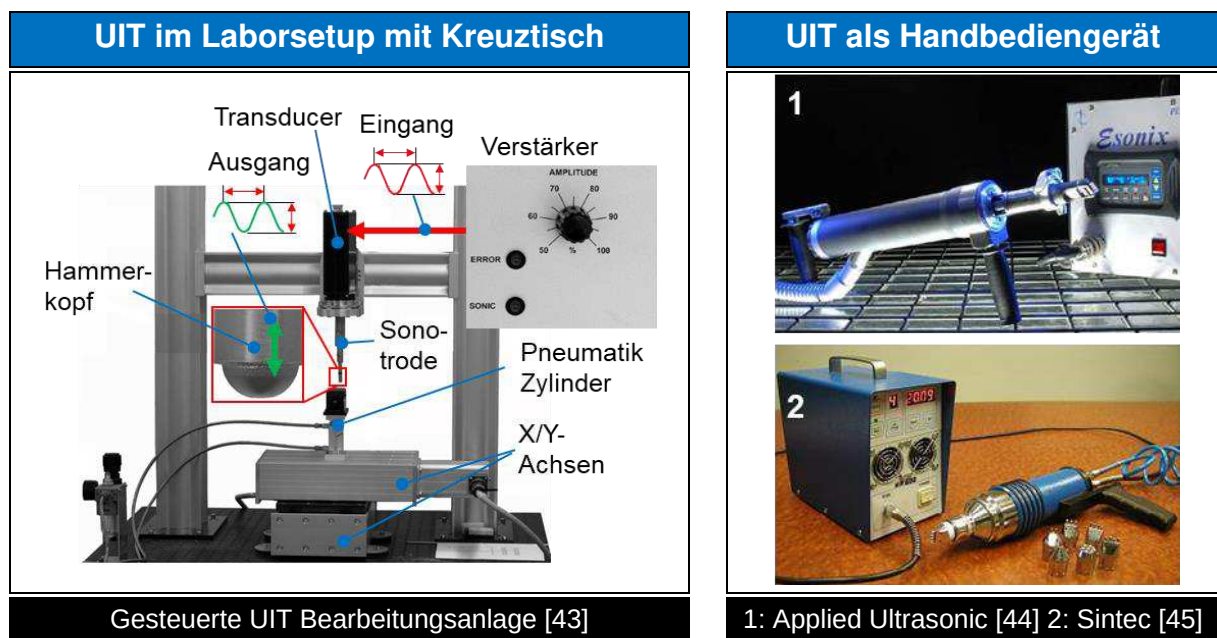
UIT-Systeme im Labor- und Handbetriebssetup, links:UIT-Anlage im Laborbetrieb, rechts: Handgeführte UIT-Systeme
